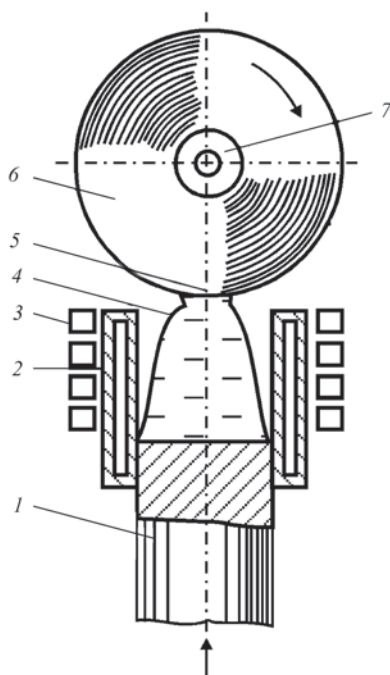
Схема получения металлических заготовок типа «диск» из расплава: 1 — расходимая заготовка; 2 — секционный кристаллизатор; 3 — индуктор; 4 — металлическая ванна; 5 — контактная зона заготовки с металлической ванной; 6 — намораживаемая заготовка (диск); 7 — затравка
